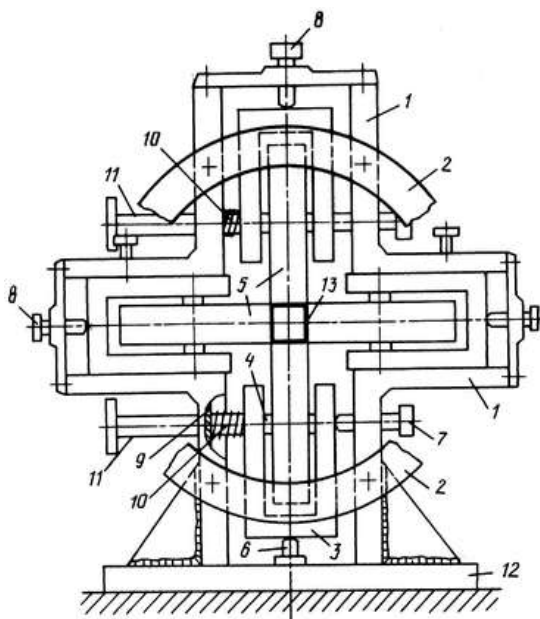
Универсальная клетка для переформовки круглой трубы в профильную: 1 – Г-образные опоры; 2 – кольца; 3 – подушки-кассеты; 4 – оси; 5 – формирующие цилиндрические валки; 6 – на регулировочный вертикальный винт; 7 – нажимные винты; 8 – регулировочные винты; 9 – наружные грани опор; 10 – упругие элементы (цилиндрические пружины); 11 – приводная часть осей горизонтальных валков; 12 – опорная плита
